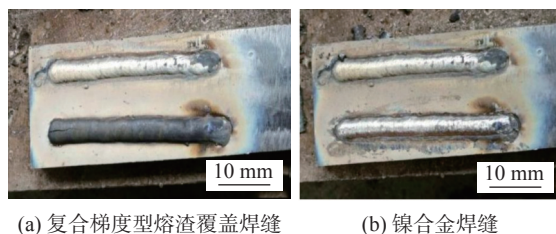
复层梯度型熔渣辅助镍合金焊缝形貌
